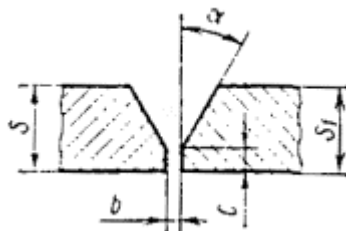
Конструктивные элементы подготовленных кромок свариваемых деталей
